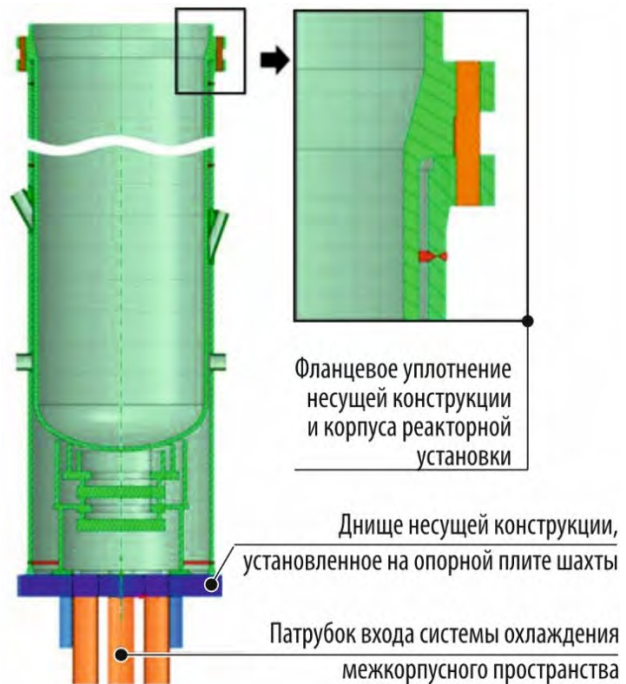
Вид в разрезе нового корпуса внутри несущей конструкции реактора
